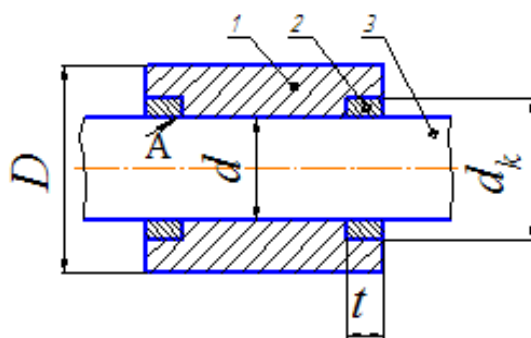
Прессовое соединение со вставными кольцами: 1- ступица; 2 – вставное кольцо; 3 – вал
